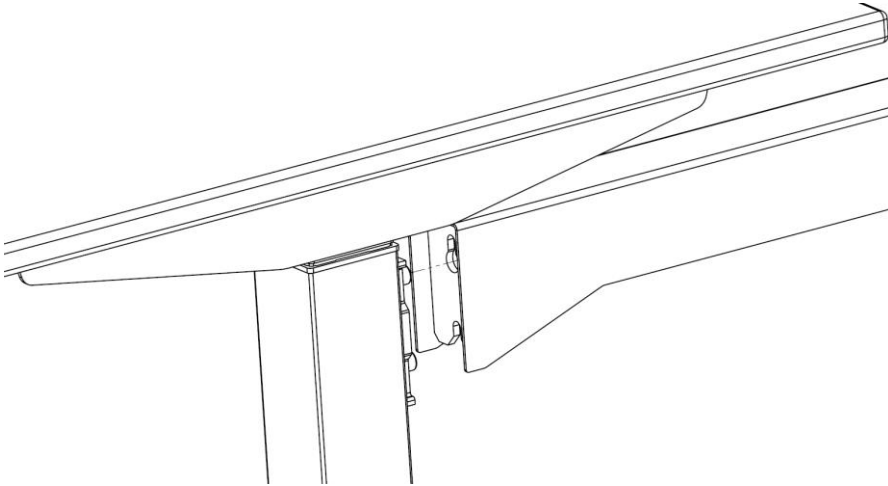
Position Innensechskantschraube zu Verbinder Bench
